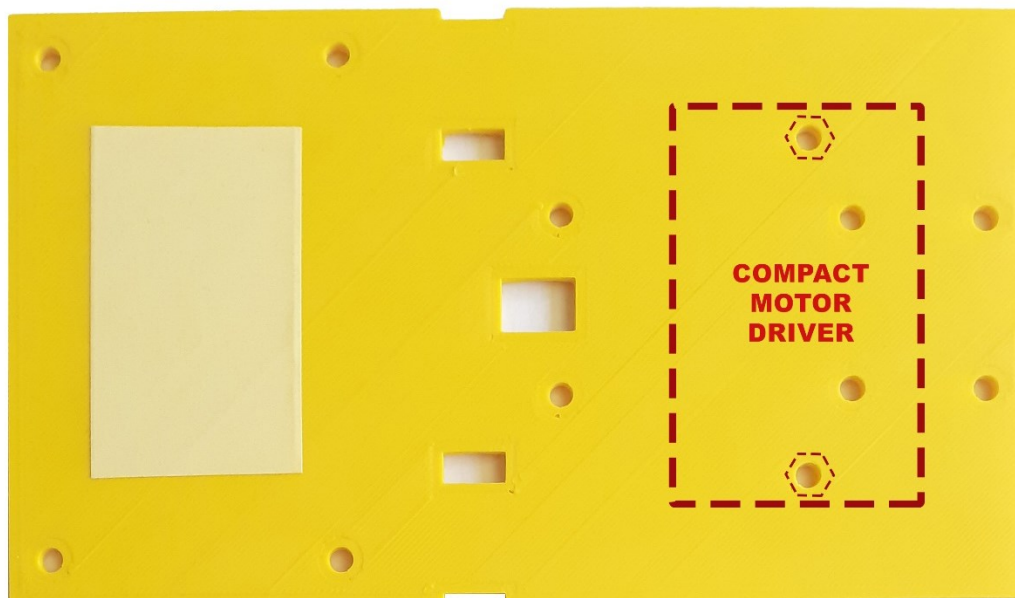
Figura 14: Diagrama mostrando onde o driver de motor compacto será colocado
